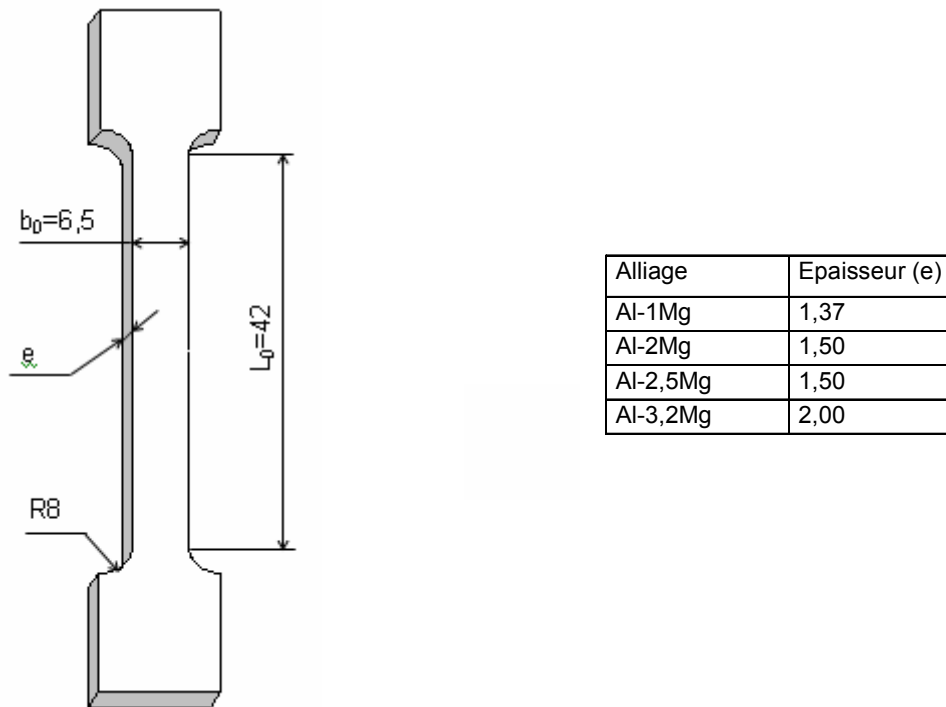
Dimensions des éprouvettes d'essais (en mm).
